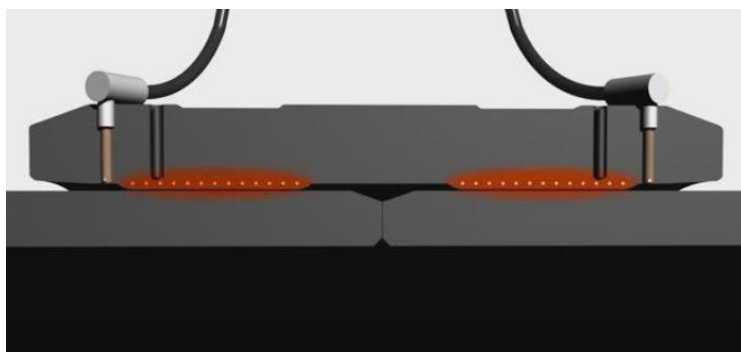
Ligação electro soldada em PEAD
